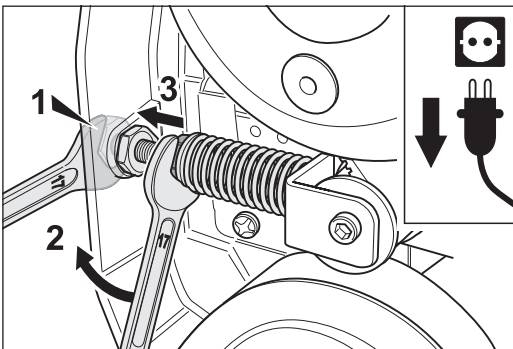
Die Schraube des Zahnriemenspanners mit einem Gabelschlüssel festhalten (1) und gleichzeitig mit einem zweiten Gabelschlüssel die Spannmutter bis an die Kontermutter schrauben (2 + 3).
